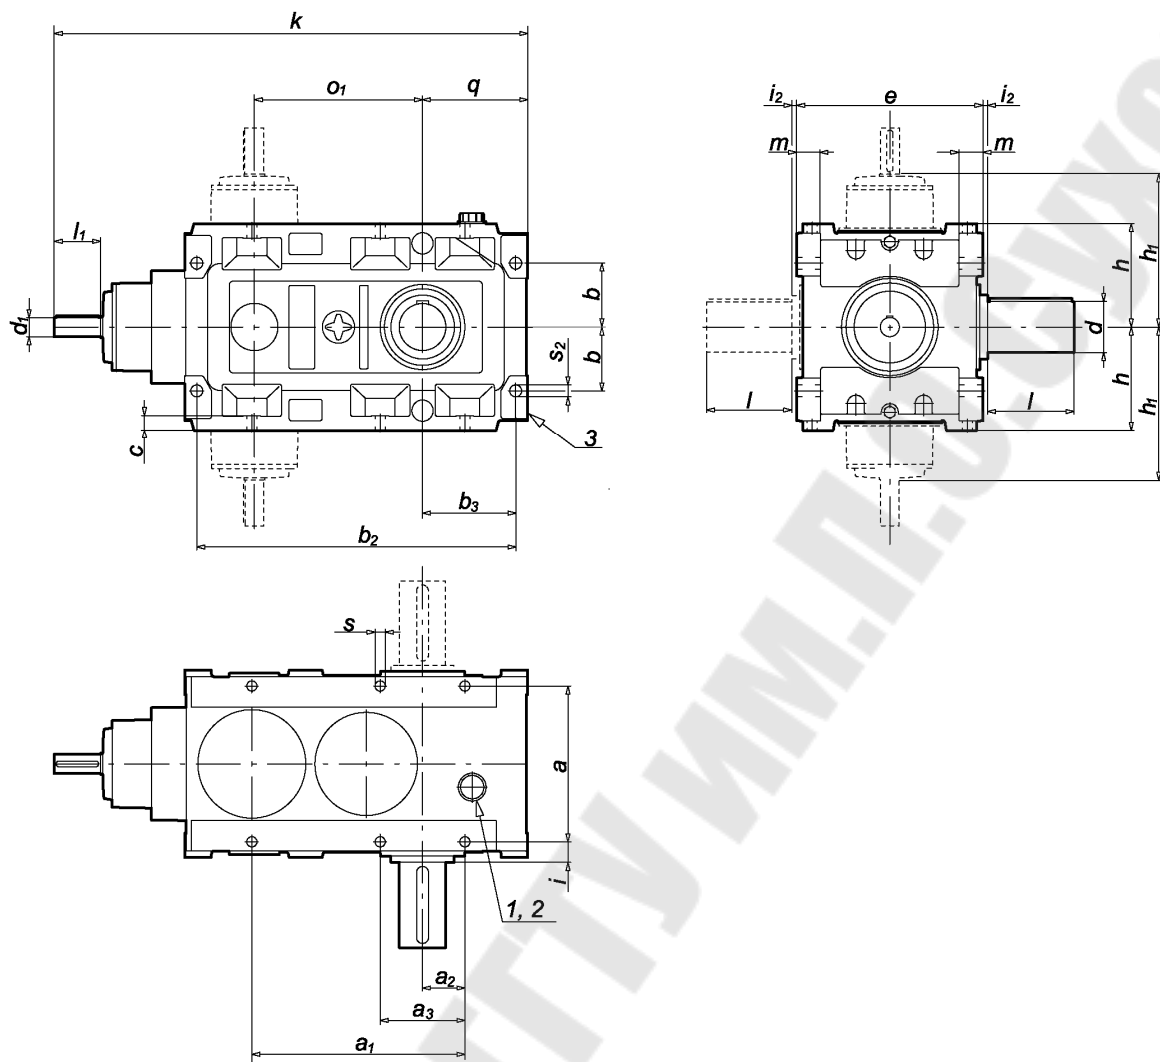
Редукторы трехступенчатые 5КЦ2 – 180...280ES, на лапах:
